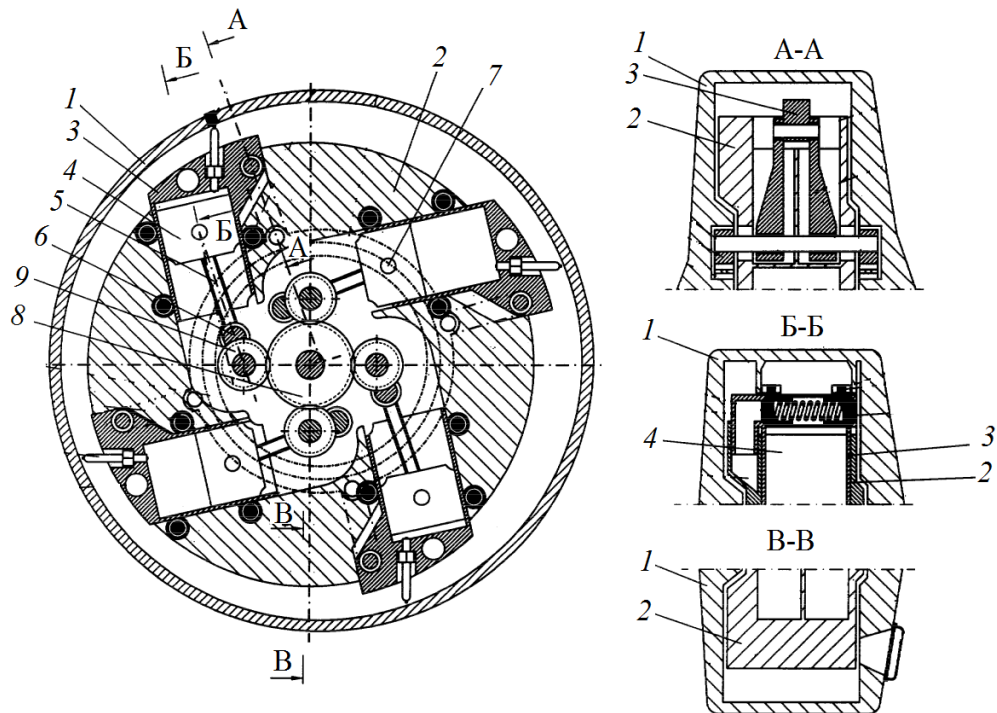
Загальна будова роторно-поршневого двигуна внутрішнього згоряння [123]: 1 – корпус двигуна; 2 – блок циліндрів, що обертається; 3 – плаваючий циліндр; 4 – поршень; 5 – шатун; 6 – кривошип; 7 – поршневий палець; 8 – блок шестерень; 9 – шестірня
